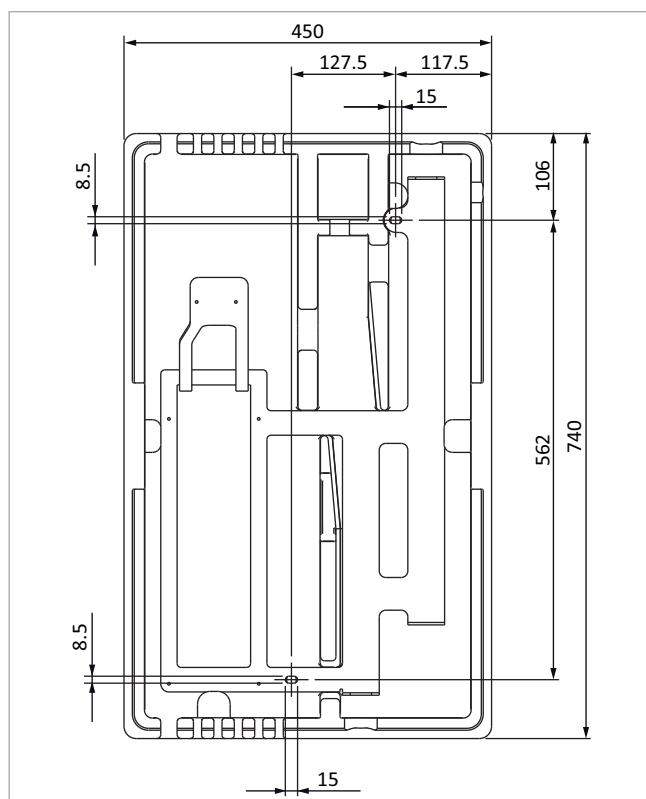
Bohrschablone / Maße für Bohrlöcher
